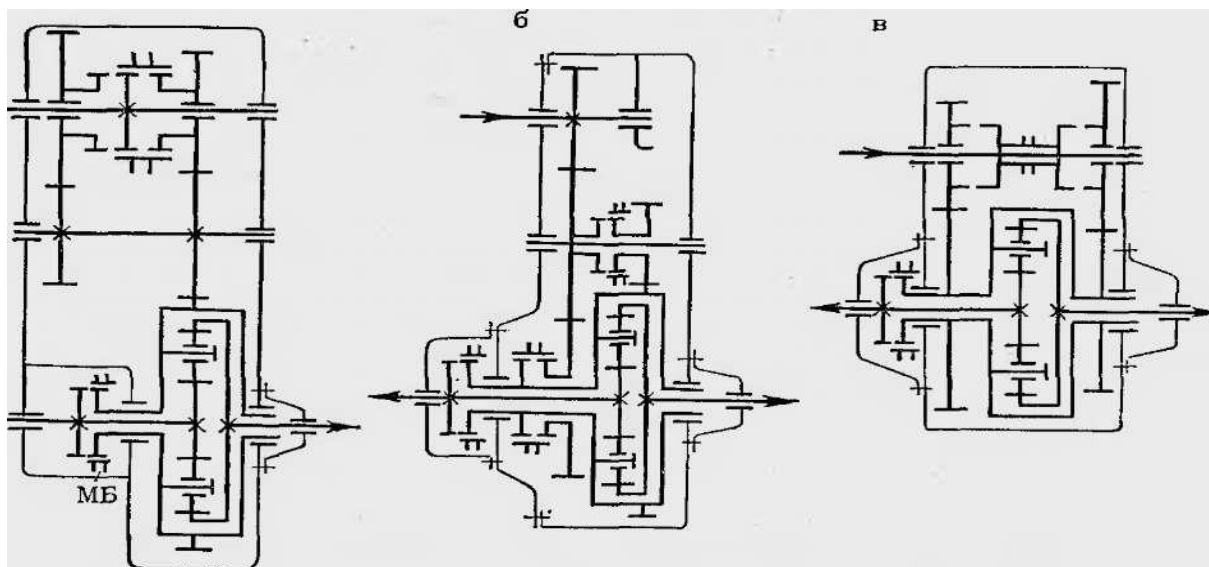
Схемы раздаточных коробок с дифференциальным приводом: а - УРАЛ-375; б - КамАЗ-4310; в - Zahnradfabrik «VG-275. 380, 800»
